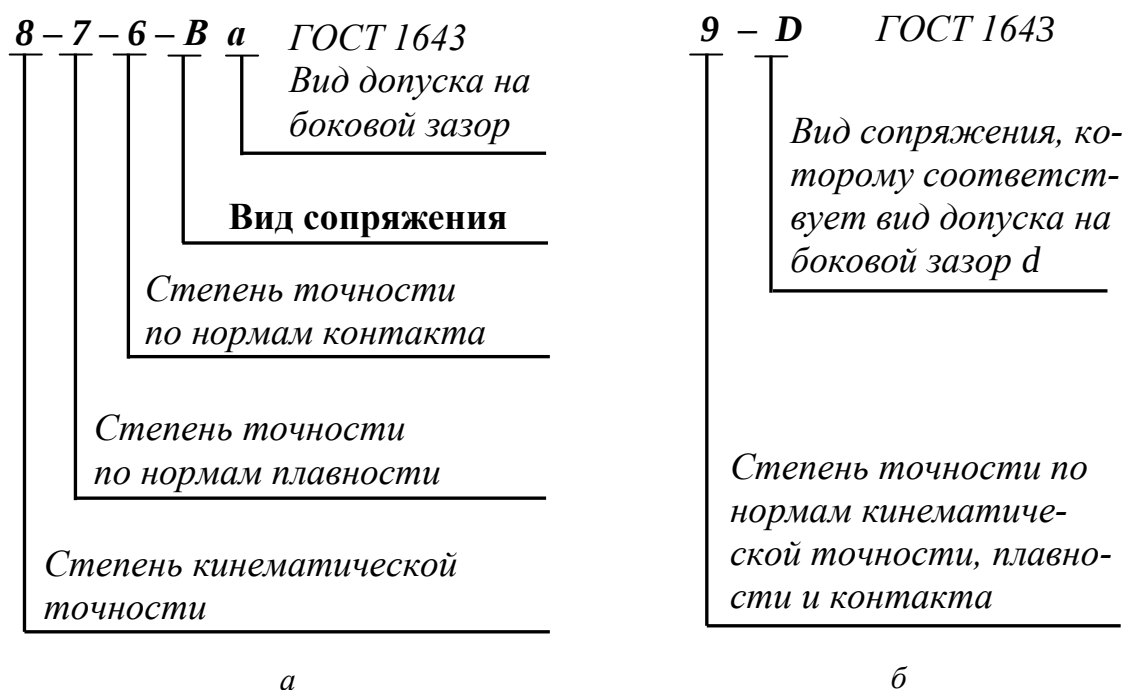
Обозначение точности зубчатых колес и передач:
